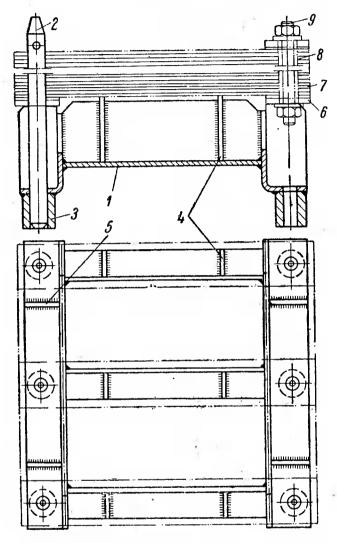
Приспособление для сборки магнитопровода типа ТСВ-1,5/0,5.
